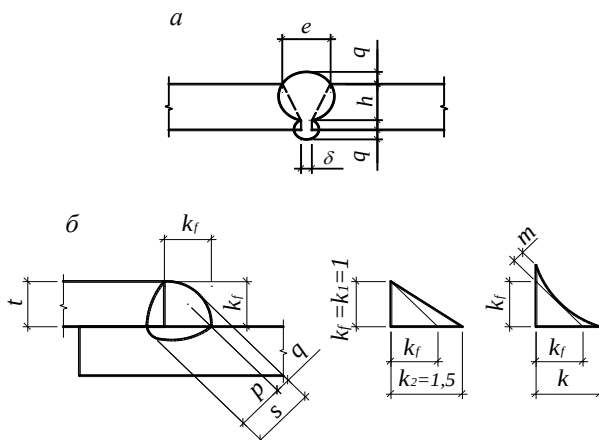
Форма и геометрические размеры сварного шва:
